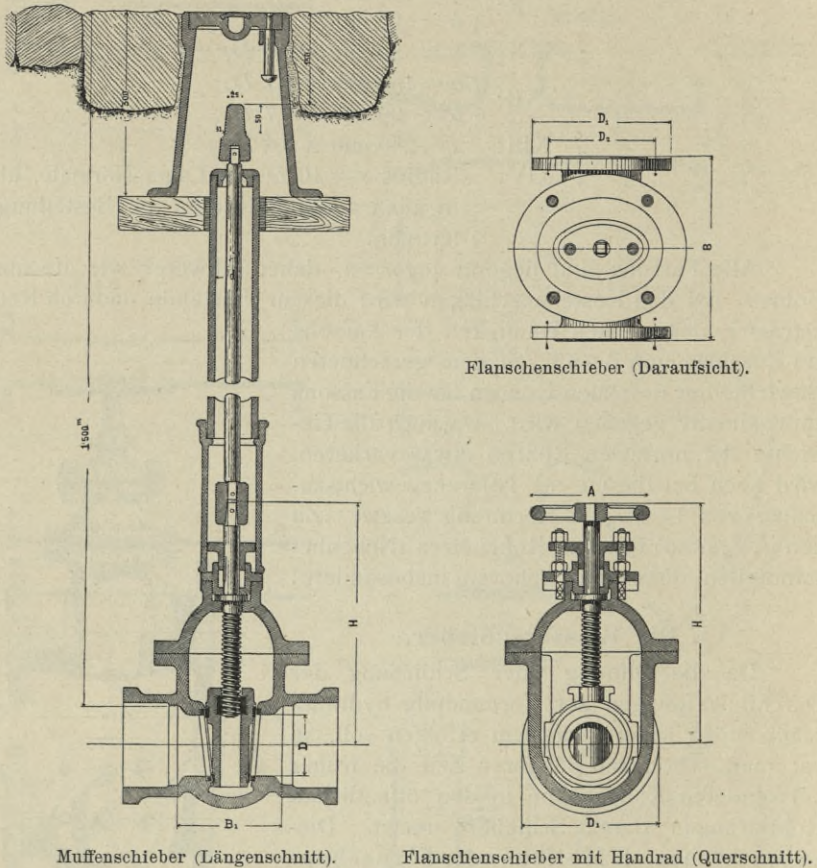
Schieber mit Handrad oder Einbaugarnitur.
